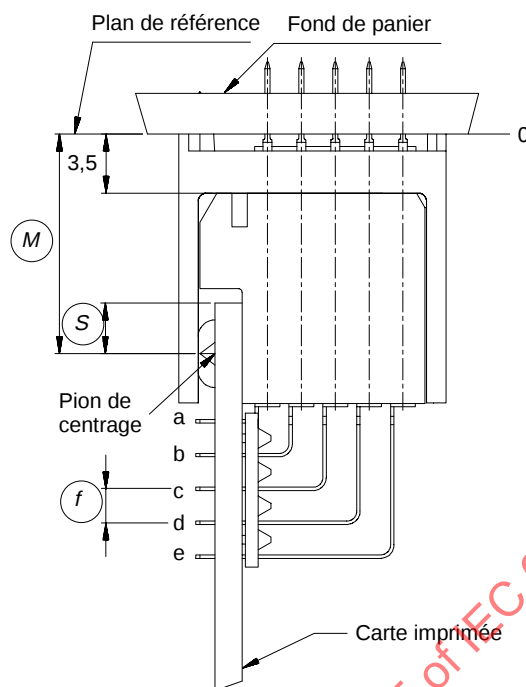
Dimensions en largeur – Boîtier de configuration 2
